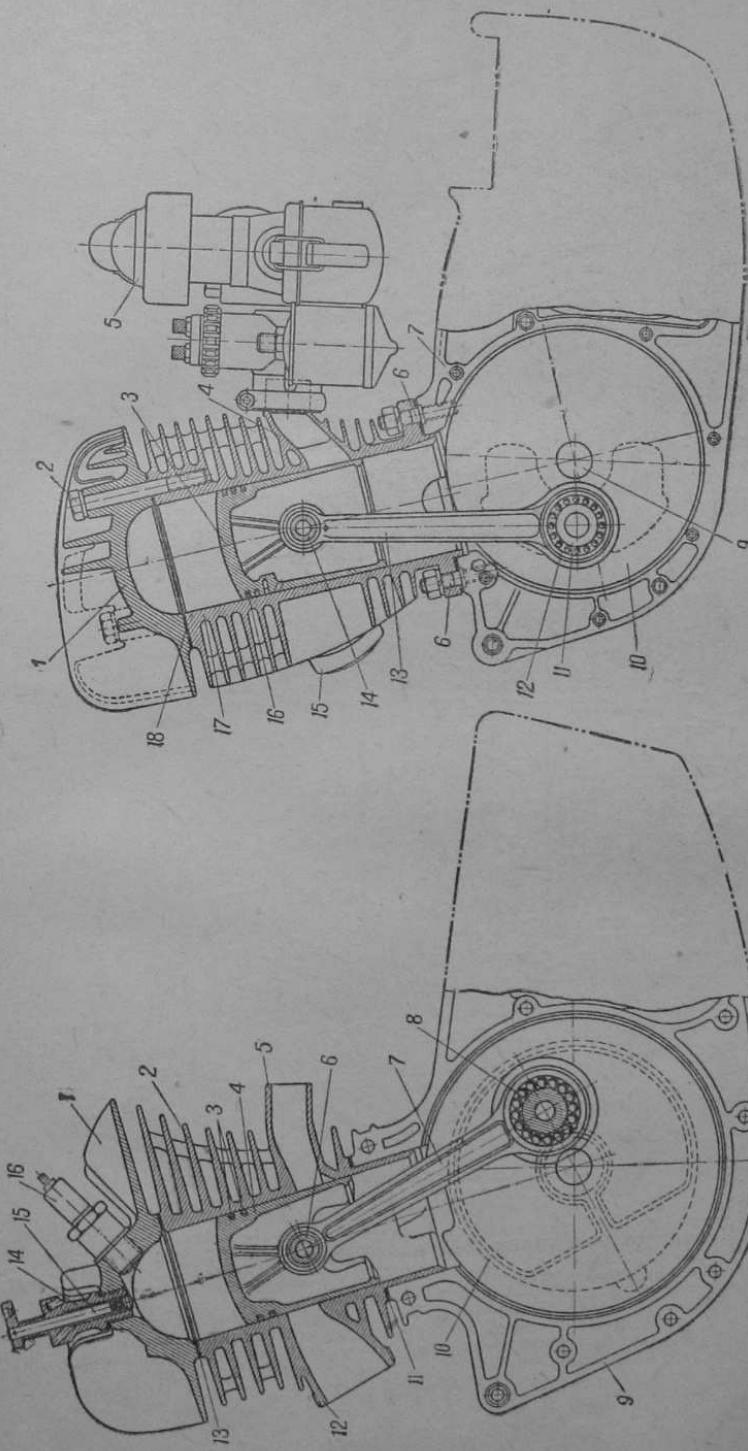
Двигатель мотоцикла М1А. Поперечный разрез:
